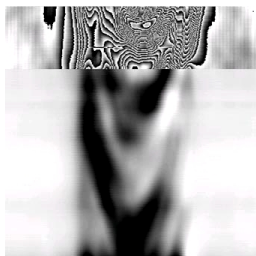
Магнитный образ сварного шва в нержавеющей стали, полученный вихретоковым методом
